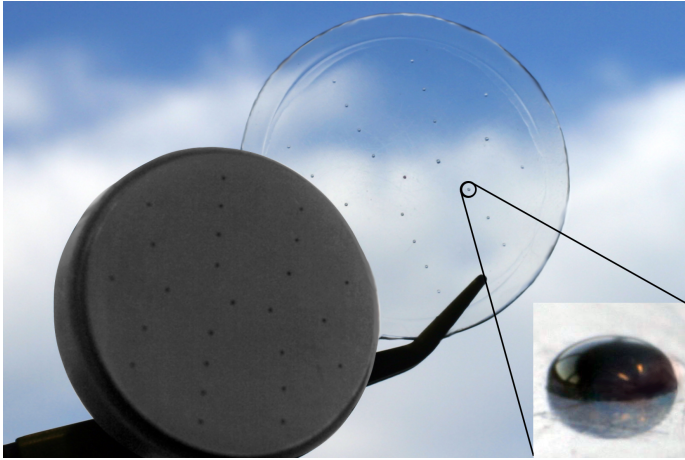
Duktilitätswerkzeug mit geprägter Glasprobe (Bild: Fraunhofer IWU)
